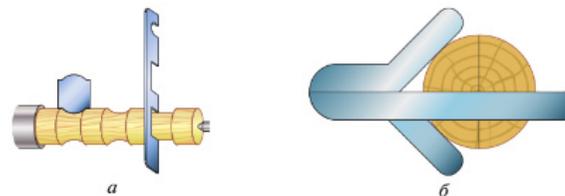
Токарные приспособления: а — образцы контрольных шаблонов; б — угловой центроискатель
